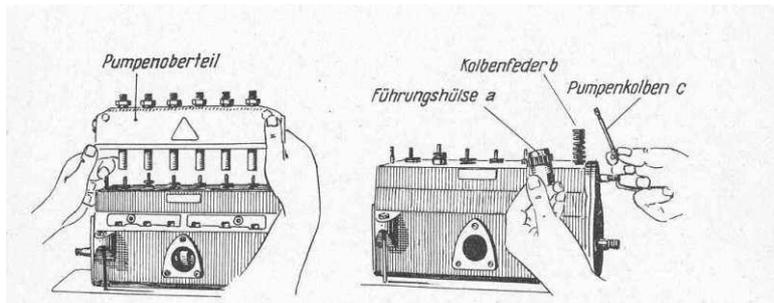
Das Pumpenoberteil wird langsam, gerade nach oben abgezogen (links) und die Pumpenkolben herausgezogen (rechts)
